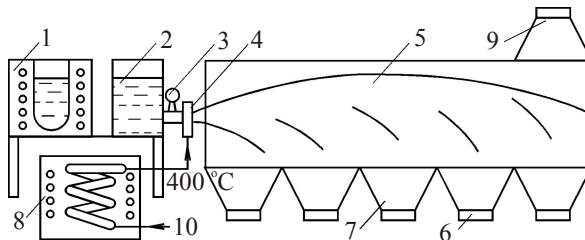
Установка для одержання порошку з індукційним плавленням металу і розпорошенням розплаву газом: 1 — піч; 2 — металоприймач; 3 — вентиль; 4 — форсунка; 5 — камера розпорошення; 6 — затвор; 7 — бункер; 8 — піч для підігріву повітря; 9 — вихід повітря; 10 — подача повітря
